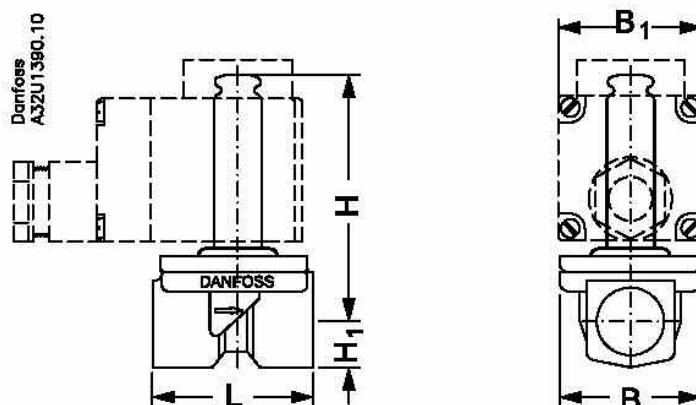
Габаритные и присоединительные размеры соленоидного клапана.
